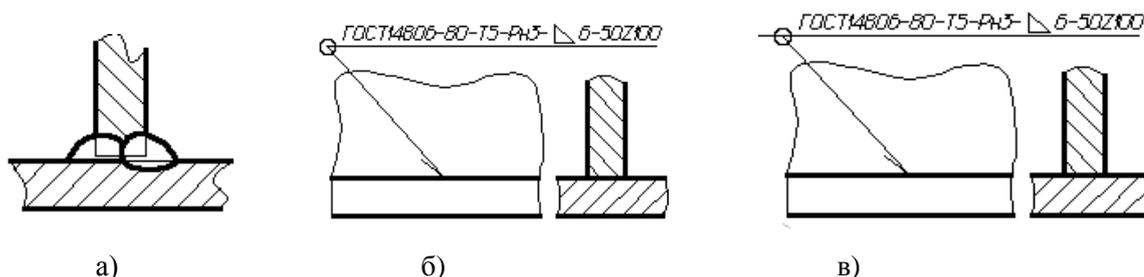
Шов таврового соединения без скоса кромок: а) форма поперечного сечения шва; б) с лицевой стороны; в) с оборотной стороны
